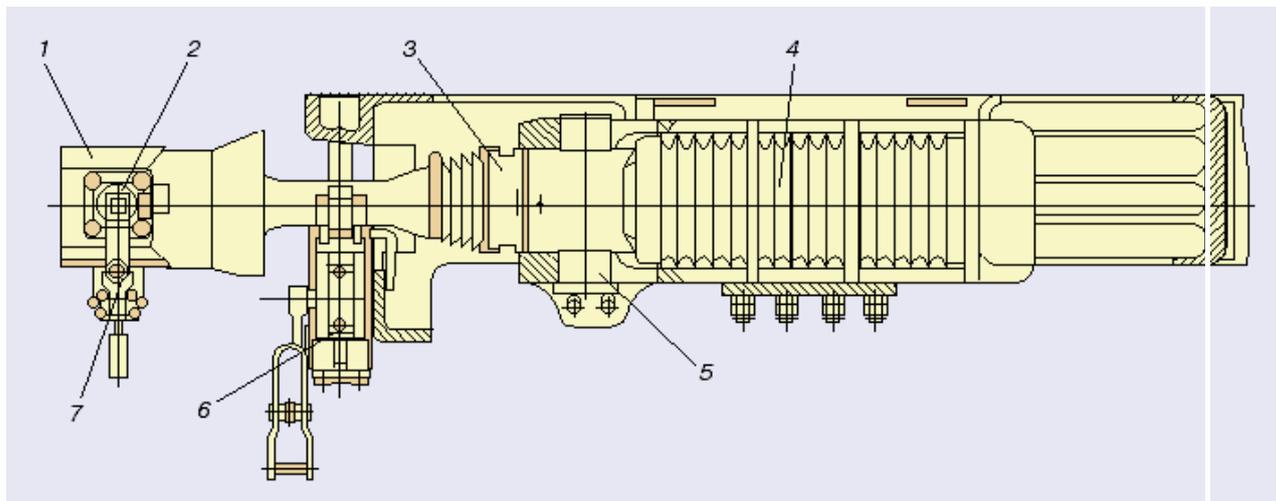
Автосцепное устройство БСУ-3 для пассажирских вагонов локомотивной тяги (без направляющего элемента): 1 — корпус; 2 — механизм сцепления (замок); 3 — шарнирный узел с шаровой опорой; 4 — поглощающий аппарат; 5 — клин тягового хомута; 6 — эластичное центрирующее устройство; 7 — расцепной привод
